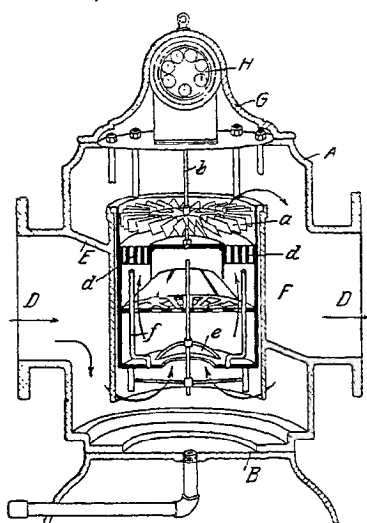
Rotary-Messer von SCHIRMER, RICHTER & Co., Leipzig.
